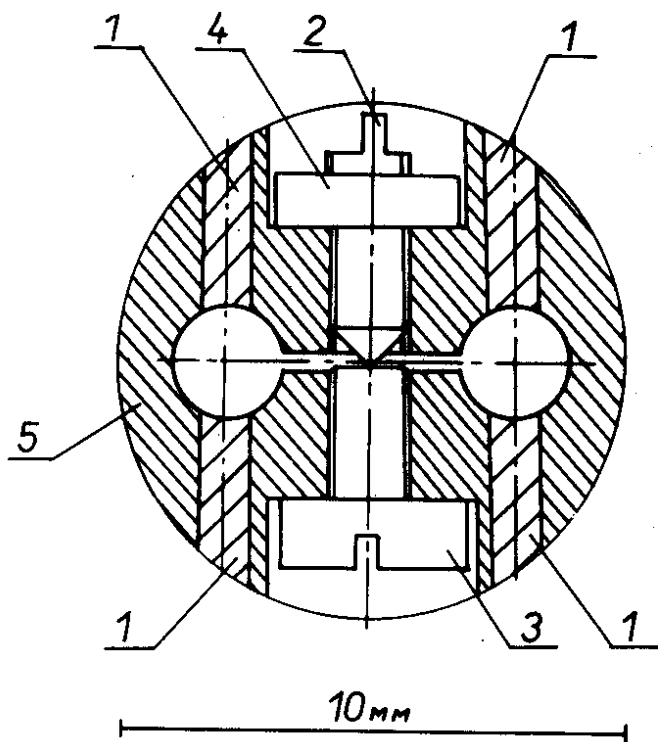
Ресквид в разрезе. 1 - резистивная вставка из меди; 2,3 - ниобиевые винты; 4 - ниобиевая гайка; 5 - корпус из ниобия.
